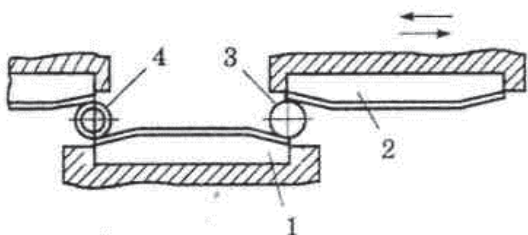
Схема накатывания резьбы плоскими плашками
